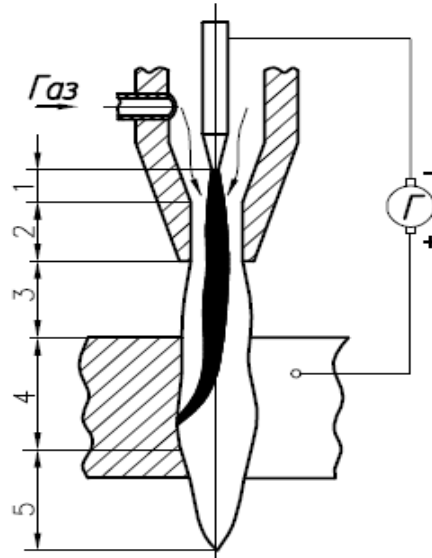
Схема плазмової дуги прямої дії та її ділянки: 1 – закрита; 2 – стисла; 3 – відкрита; 4 – робоча; 5 – факел плазми; Г – генератор струму
